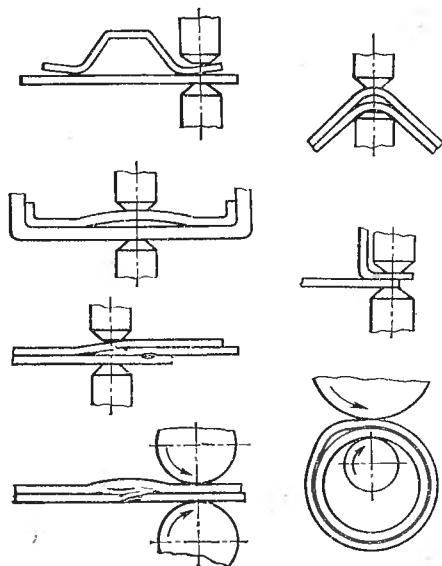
Примеры неправильной сборки деталей под сварку
